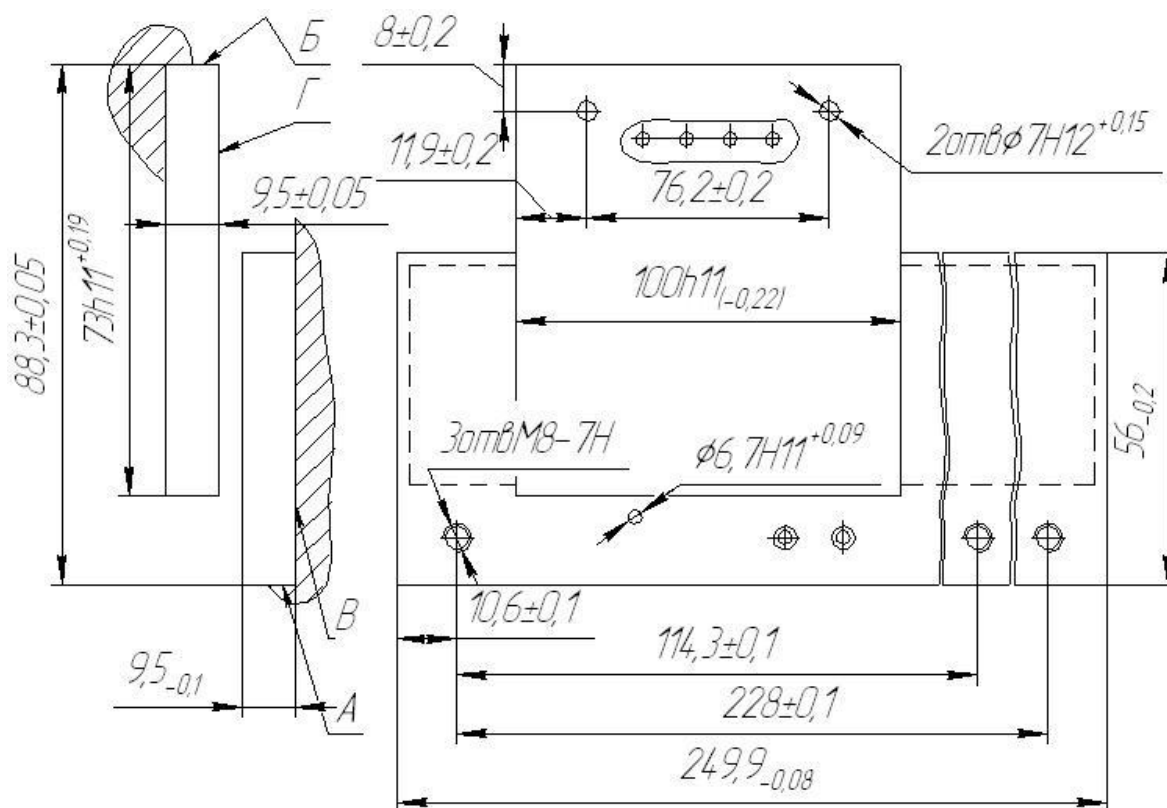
Установочные размеры и поверхности линейного индуктосина
